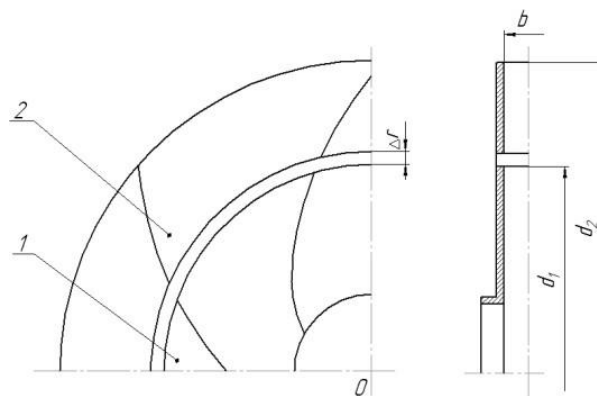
Центробежная турбомашина с коаксиальным расположением рабочих колес: 1- внутреннее рабочее колесо, 2 – наружное рабочее колесо, Δr – радиальный зазор, b – ширина колеса, d_1 , d_2 – внешние диаметры рабочих колес.
